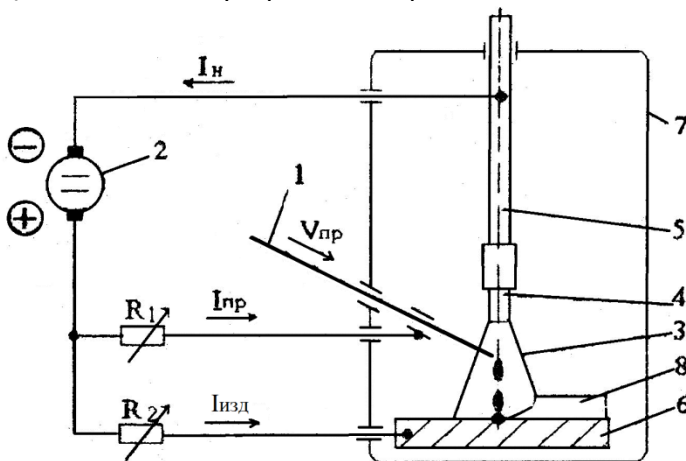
Схема наплавки ДРПК в вакууме: 1-присадочная проволока;
